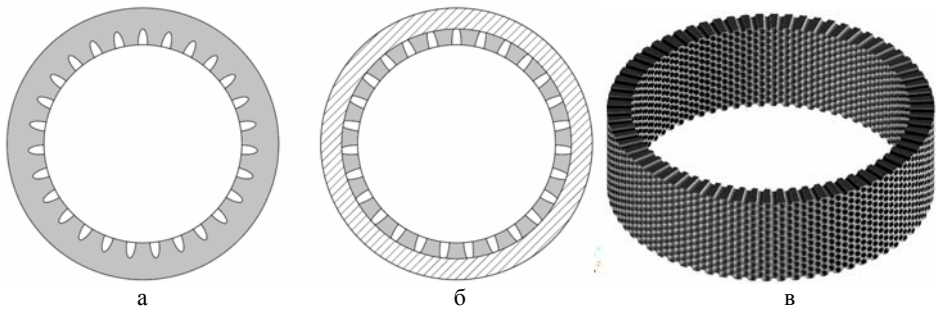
Схема макроструктуры гильзы, изготовленной путем внутреннего сканирования монолитной заготовки и последующей размерной обработки (а); составная гильза изготовленная путем запрессовки газармированного цилиндра в стальную обойму (б); вид газармированного цилиндра в пространственном изображении (в)
